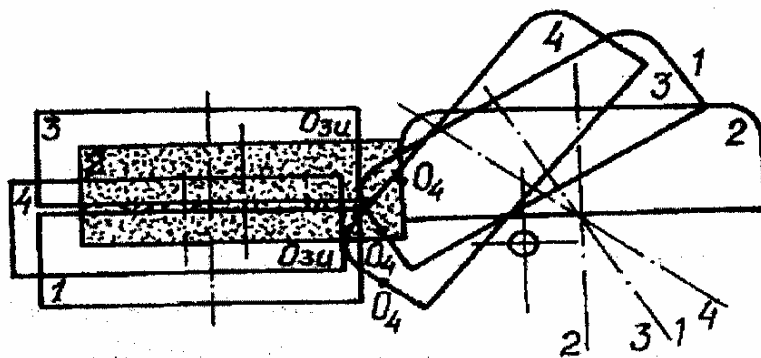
Схема положений инструмента и детали в процессе обработки (один цикл: 1, 2, 3, 4 – относительные положения инструмента и детали)
